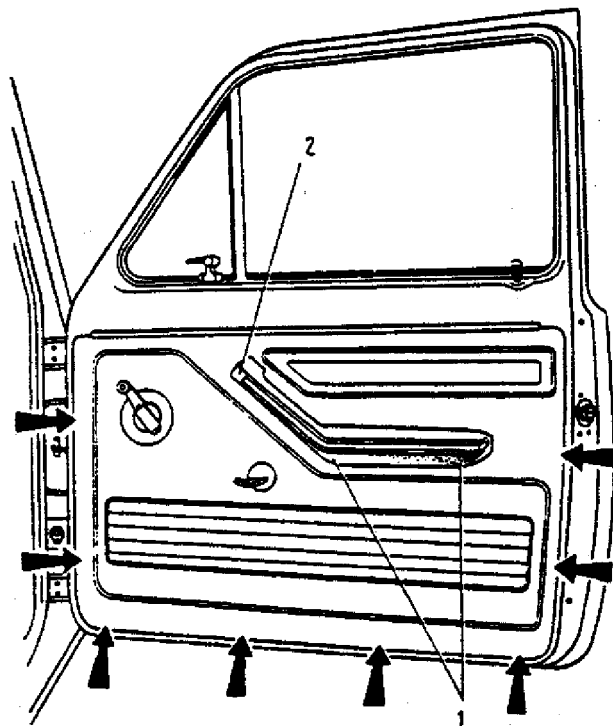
Vista do painel de acabamento interno da porta: 1 - parafusos inferiores de fixação do descanso-braço; 2 - tampa de acesso ao parafuso superior; as setas indicam as posições das presilhas de retenção do painel de acabamento ao painel interno da porta
